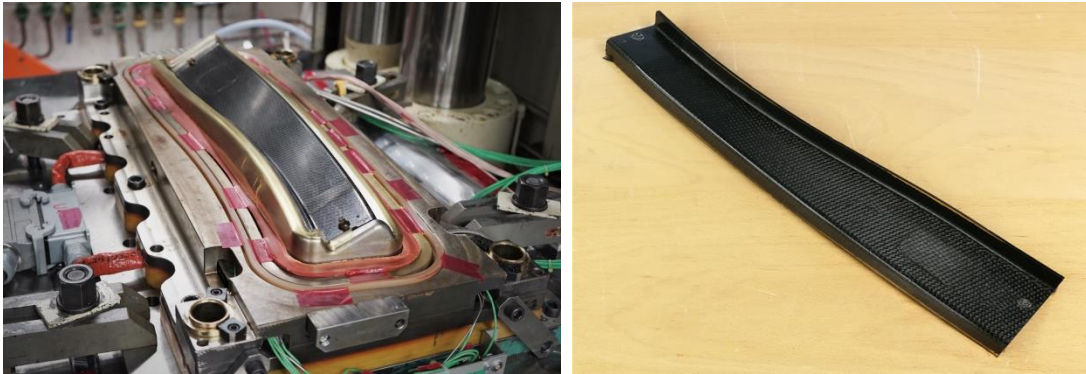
Vollständig getränktes Bauteil im Formwerkzeug (links) und Entformtes Bauteil (rechts)
